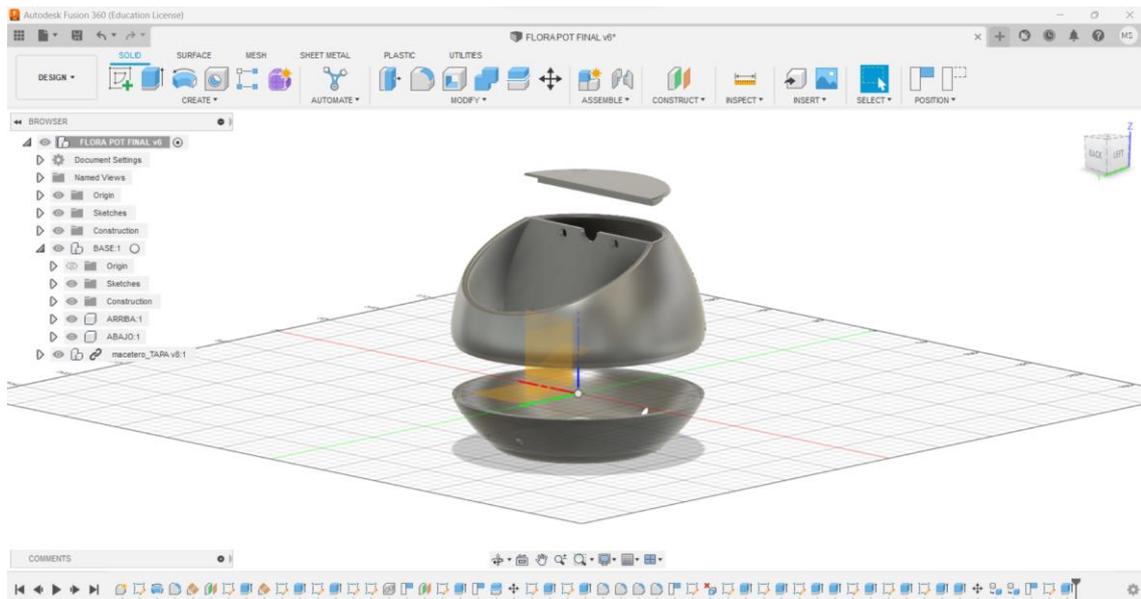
Prototipo maceta en fusión 360: partes finales
